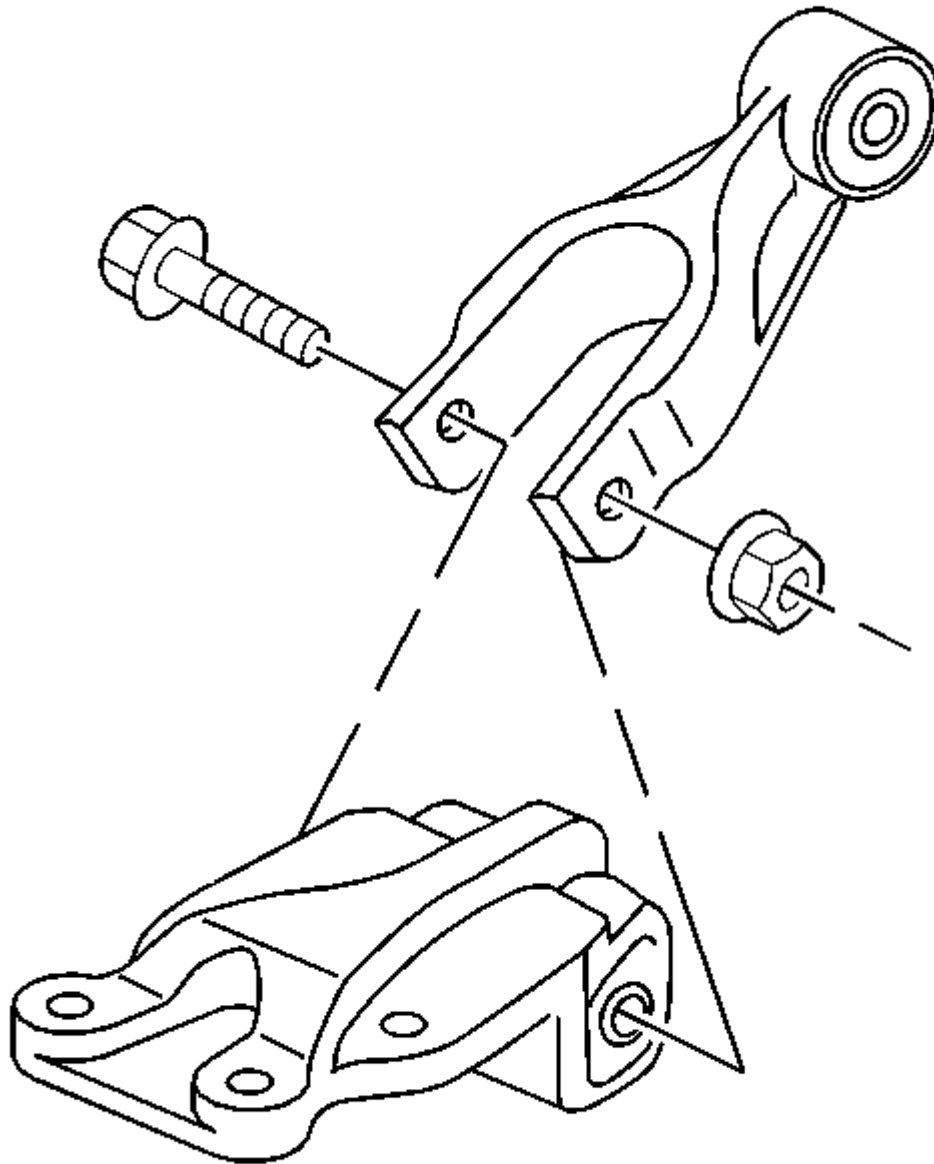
Vista del perno y la tuerca del puntero de montaje del motor en el soporte del puntero de montaje del motor en la parte superior
